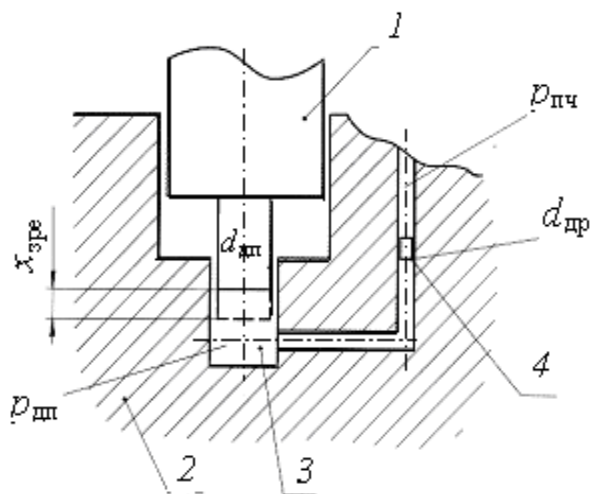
Схема для визначення сили демпфірування: 1 – запірно-регулюючий елемент; 2 – корпус гідроапарата; 3 – демпфіруюча камера; 4 – дросель
